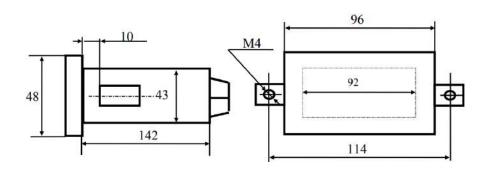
Габаритные размеры, корпус 48х96х155 мм
